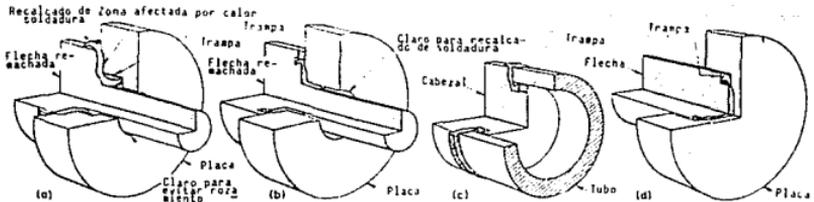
Recesos usados como trampas para recalado de soldadura en uniones soldadas por fricción.
